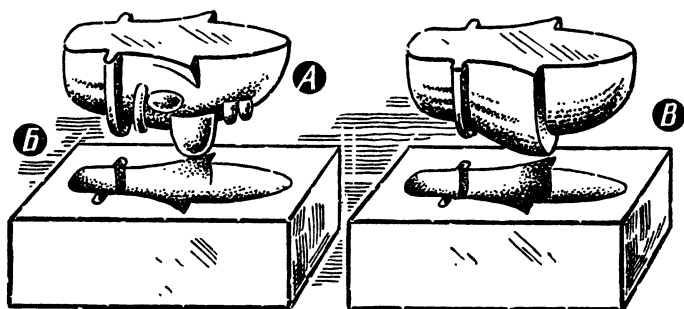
Штамповка пластмассы: А — пуансон; Б — матрица; В — пуансон и матрица для второй половинки детали.
